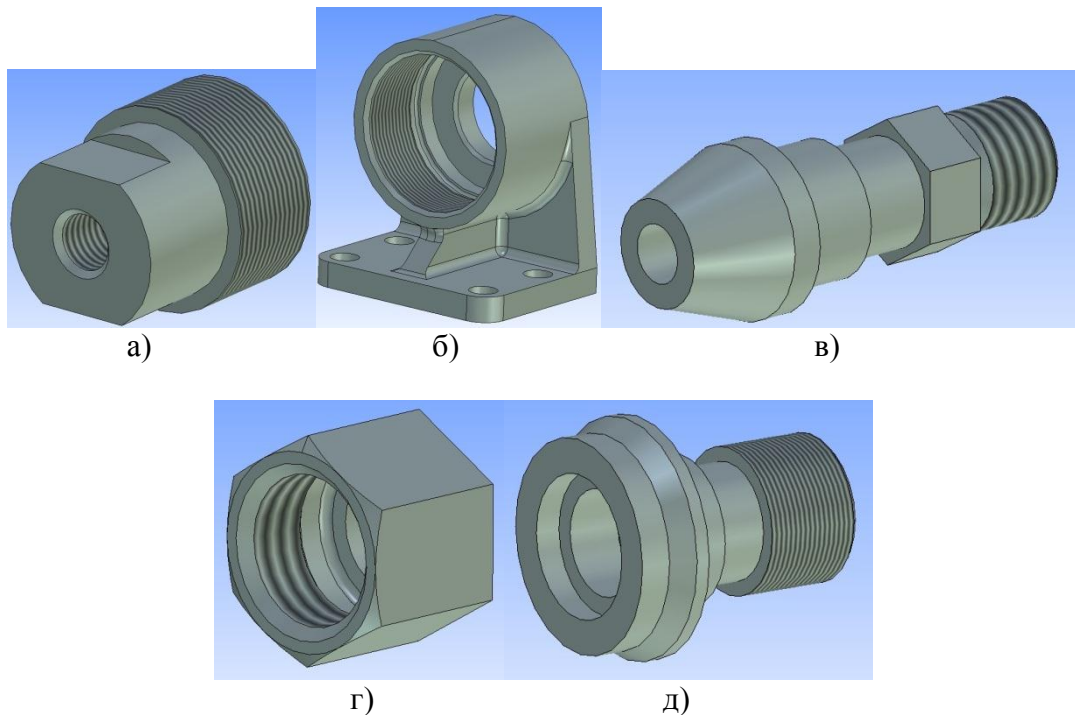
Трехмерные модели деталей сборочного узла: а – корпус; б – крышка; в – nipple; г – гайка; д – nipple
